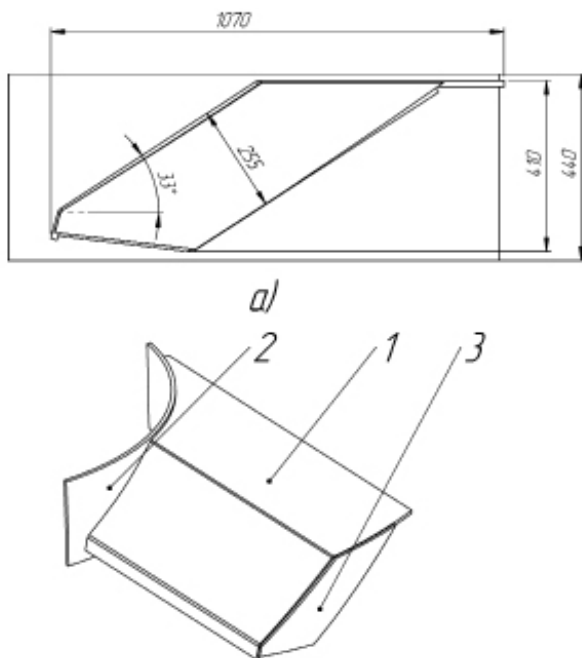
Конструкція лопаті першого ряду транспортної системи колонного дифузійного апарата КД2-А30: а) габаритні розміри лопаті; б) загальний вигляд лопаті: 1 – корпус лопаті, 2 – накладка на вал, 3 – торцевий лист
